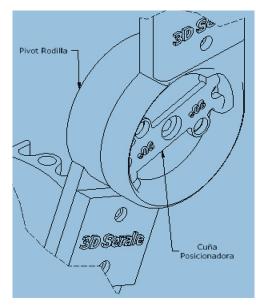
Vista isométrica detalle pívot con cuña de inmovilización. Fuente: Elaboración propia
